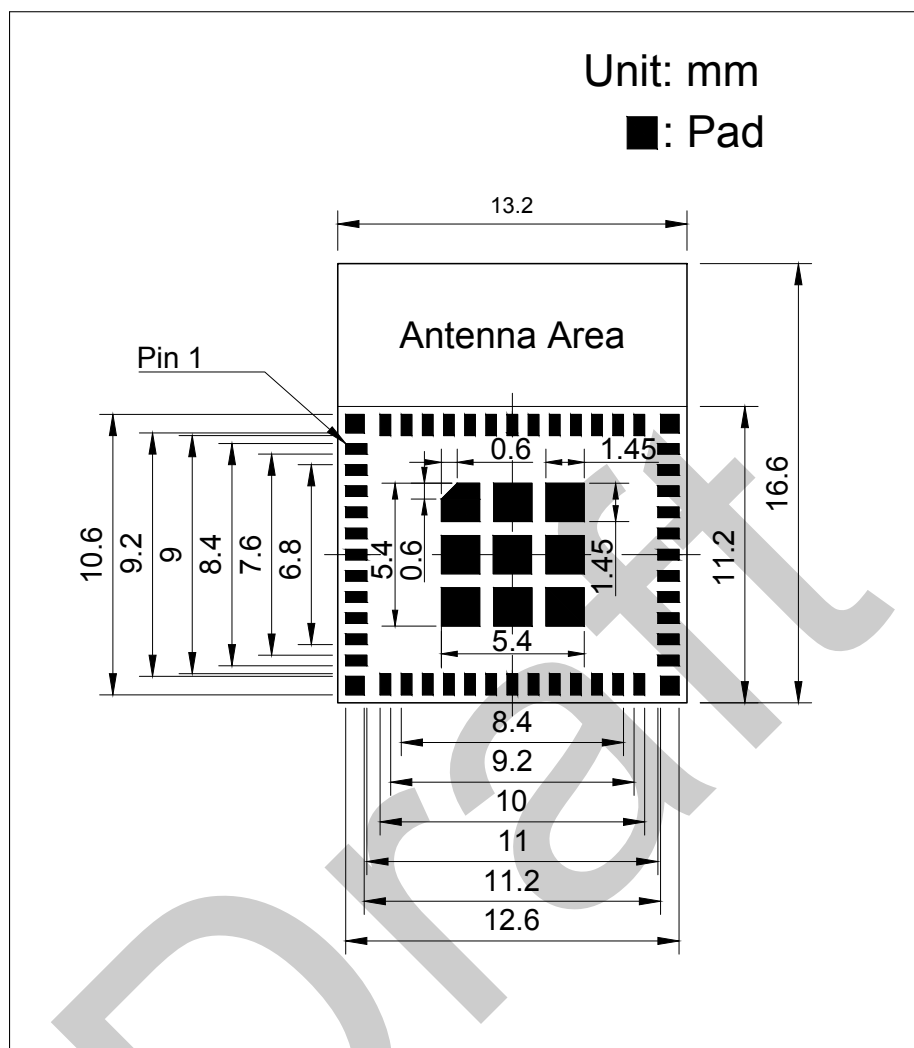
ESP32-PICO-MINI-02 PCB 封装图形
